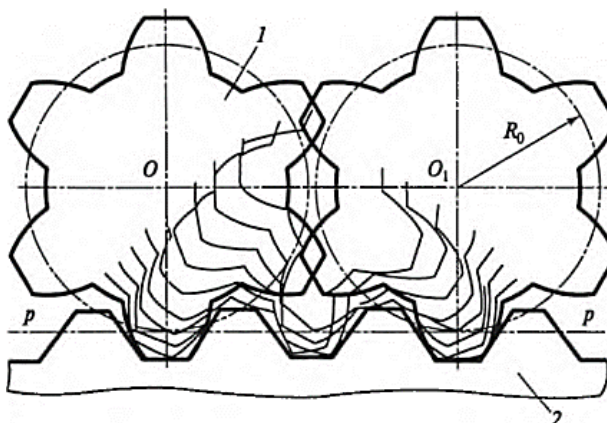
Последовательное положение зубьев колеса при качении по рейке
